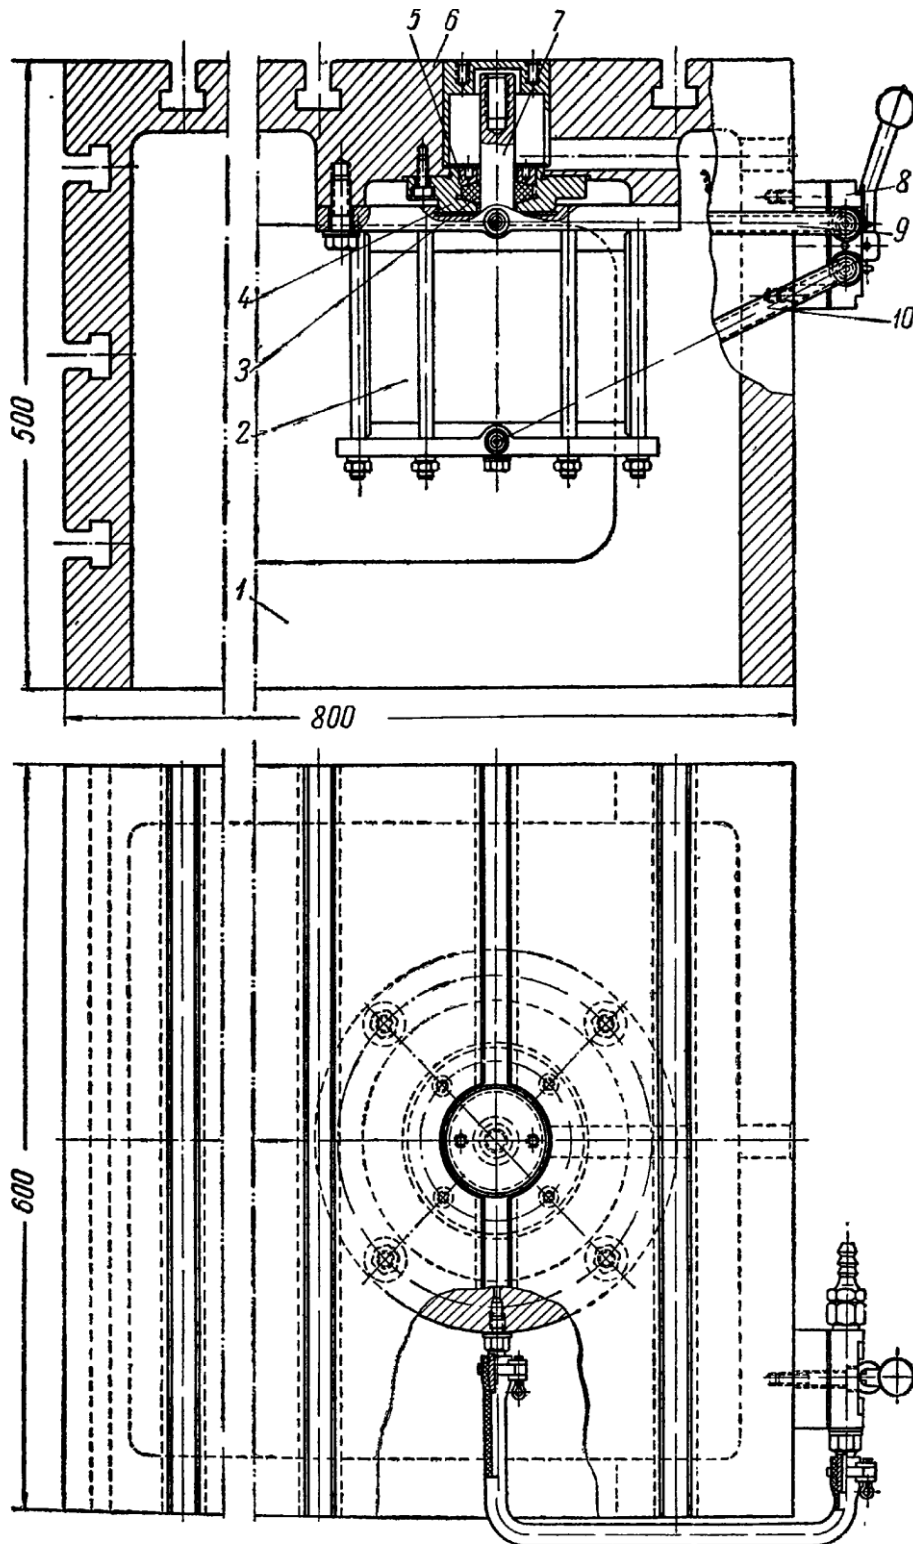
Пневмозатискний стіл для радіально-свердильного верстату
